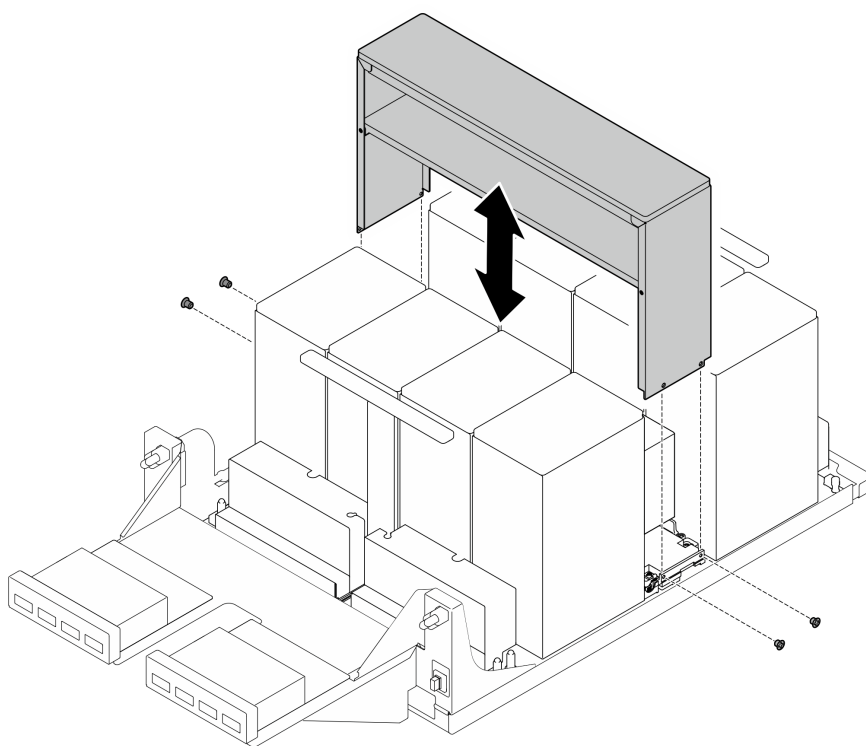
Installation du cache du dissipateur thermique NVSwitch
